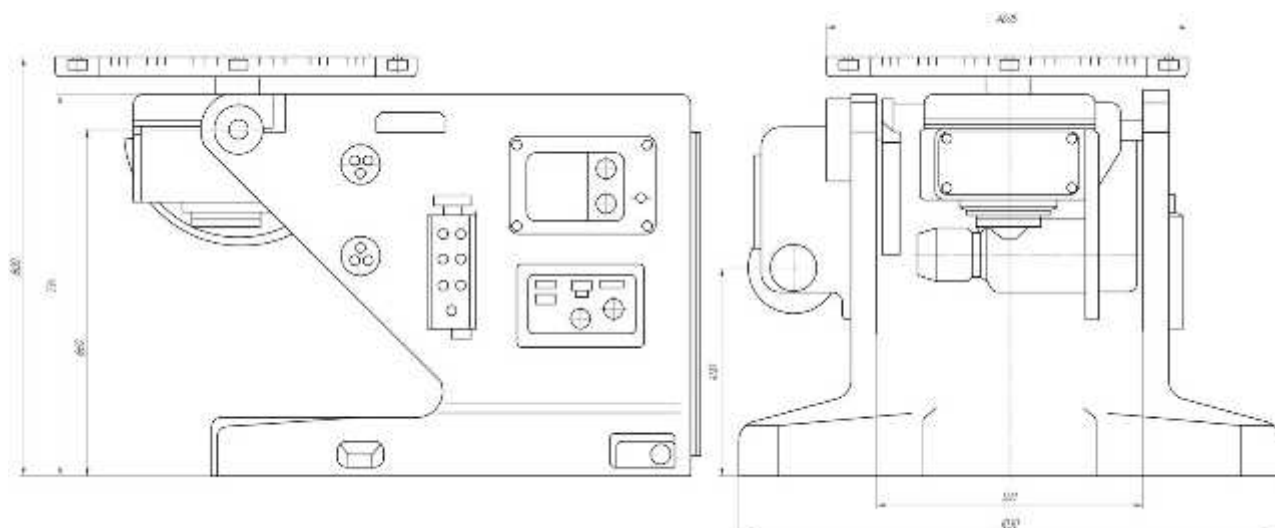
Общий вид манипулятора IRBP 250A
